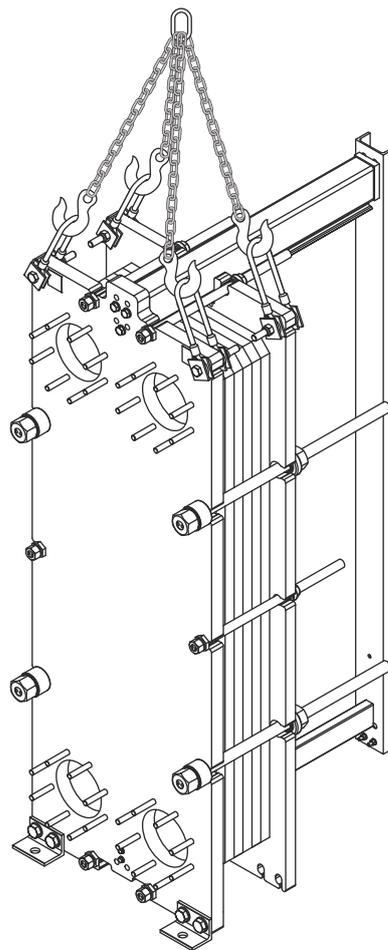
Cabo de elevação montado com uma placa de estrutura.
